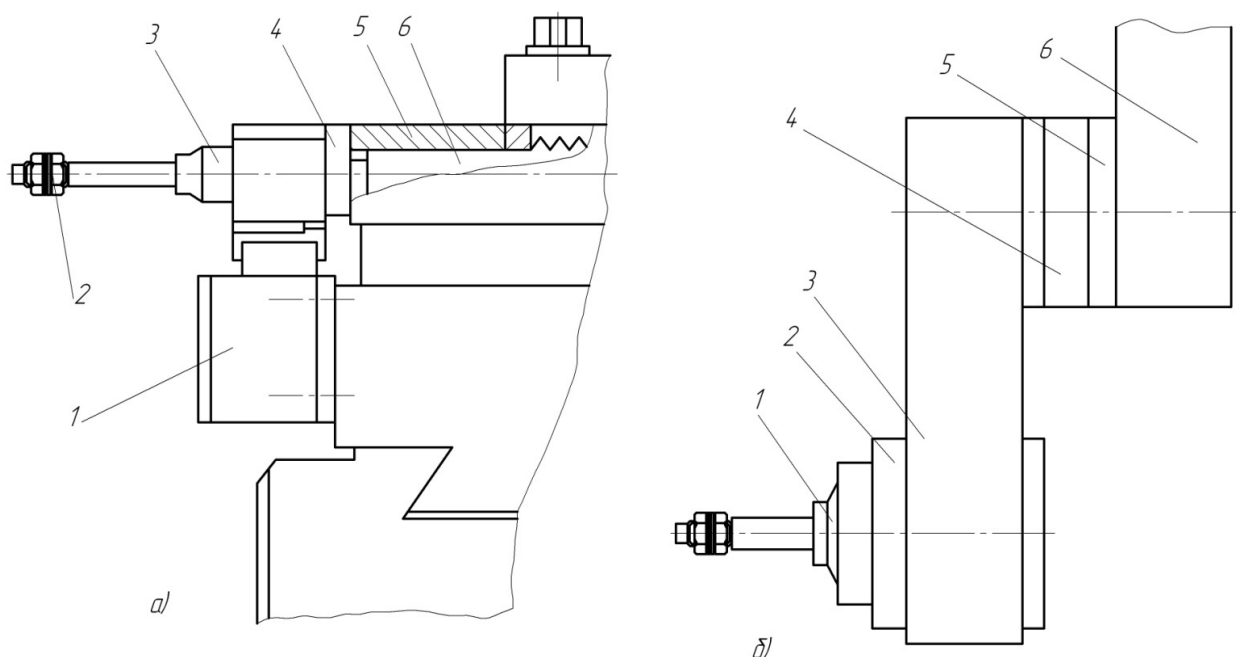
Використання вимірювальних головок для вимірювання розміру обробки в револьверних головках з вертикальною і горизонтальною осями повороту
